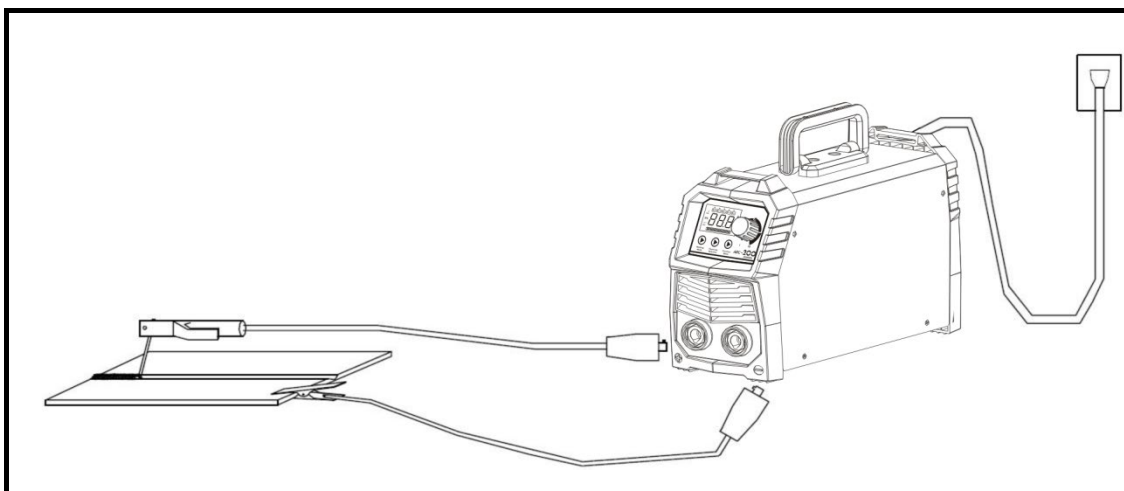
Diagrama esquemático de la soldadura MMA
